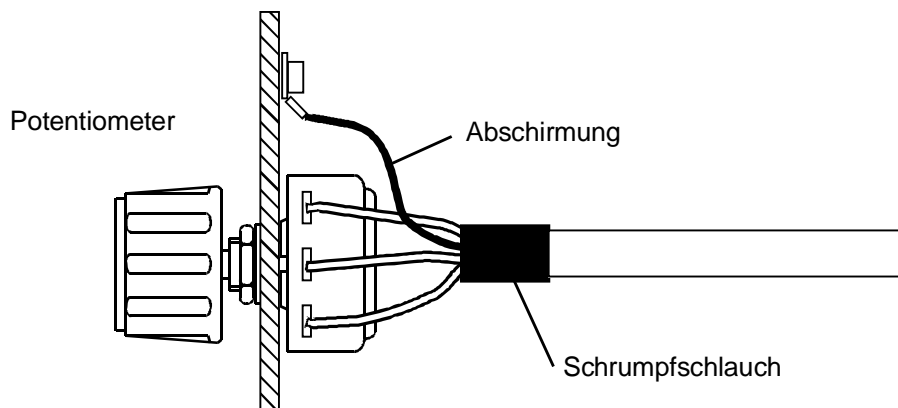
Beispiel einer Schirmbefestigung ohne Stecker
